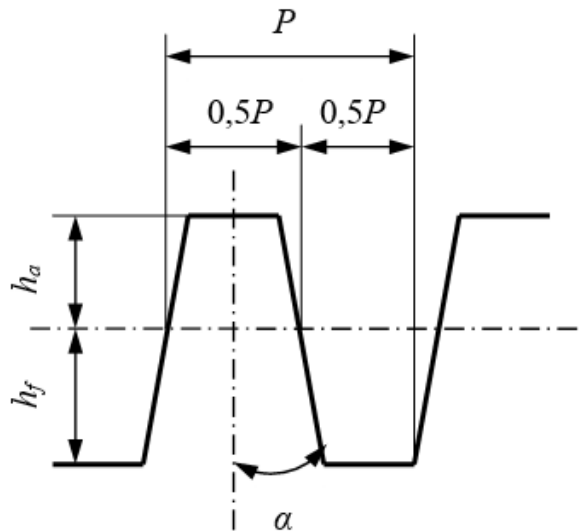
Похідний контур евольвентних зубчастих колеса
